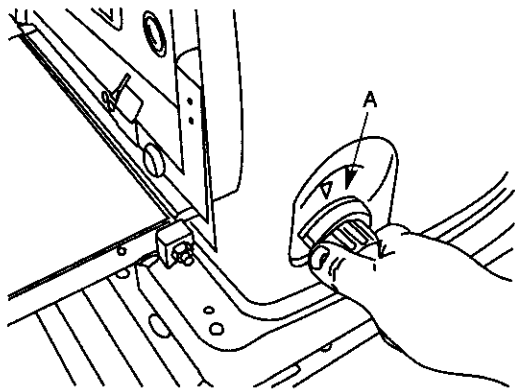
Calibrador Preajustado del Espesor de la Pieza de Trabajo
